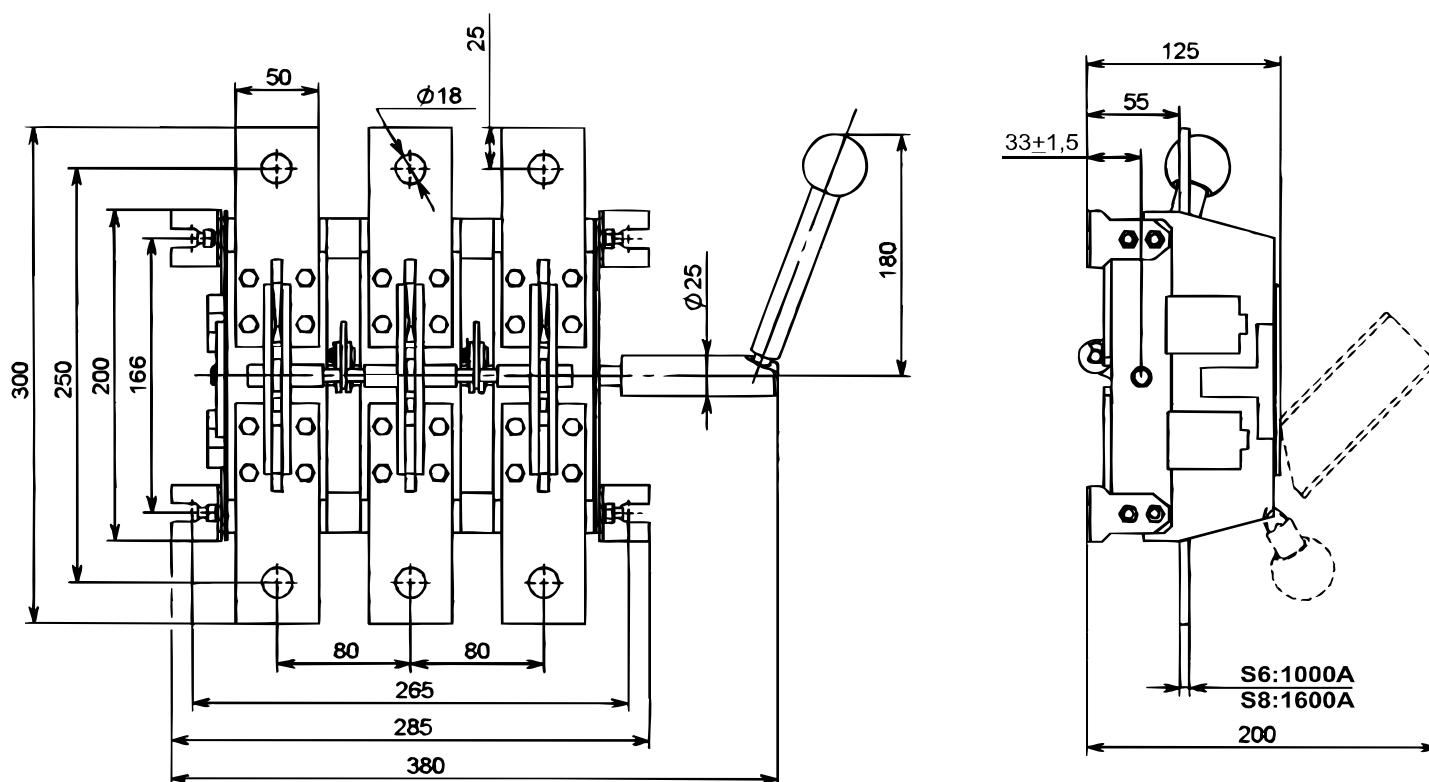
Разъединитель PE19-41(43)-31150-00 УХЛЗ с боковой смещенной рукояткой
